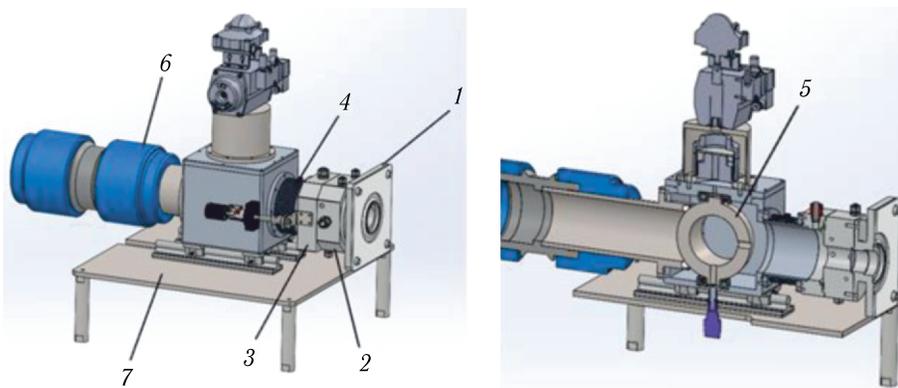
Устройство удержания мишени: 1 — фланец фиксации вакуумной фольги; 2 — фланец гелиевых каналов; 3 — фланец стыковки; 4 — сильфон тарельчатый; 5 — шаровый механизм в корпусе; 6 — прижимной фланец с компрессионным фитингом; 7 — плата с направляющими
